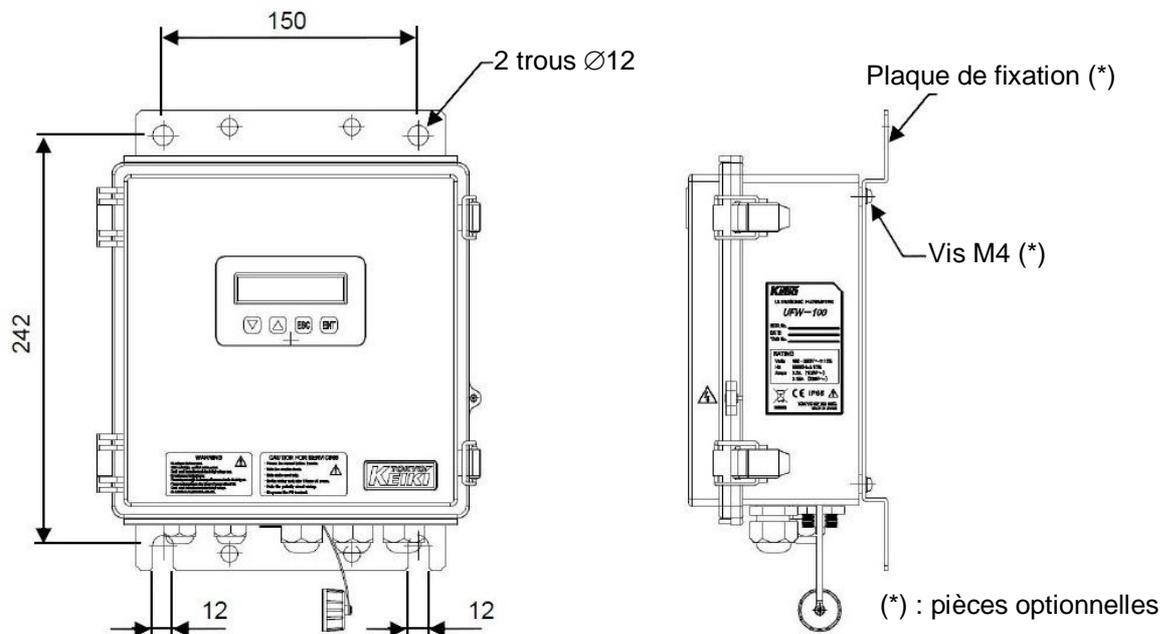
Fixation contre le mur (plaque de fixation, pièces optionnelles)
